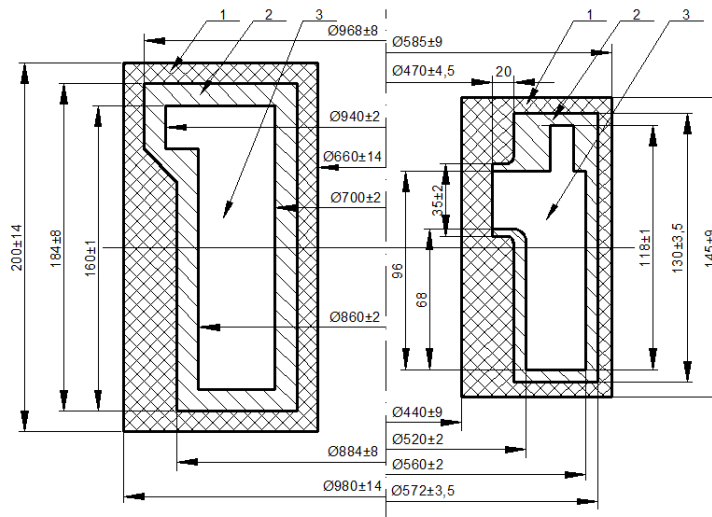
Сечения кольцевых деталей и поковок из сплава 5В (слева) и стали 45: 1, 2 – поковки, кованые на прессе и раскатанные на стане; 3 – детали.
